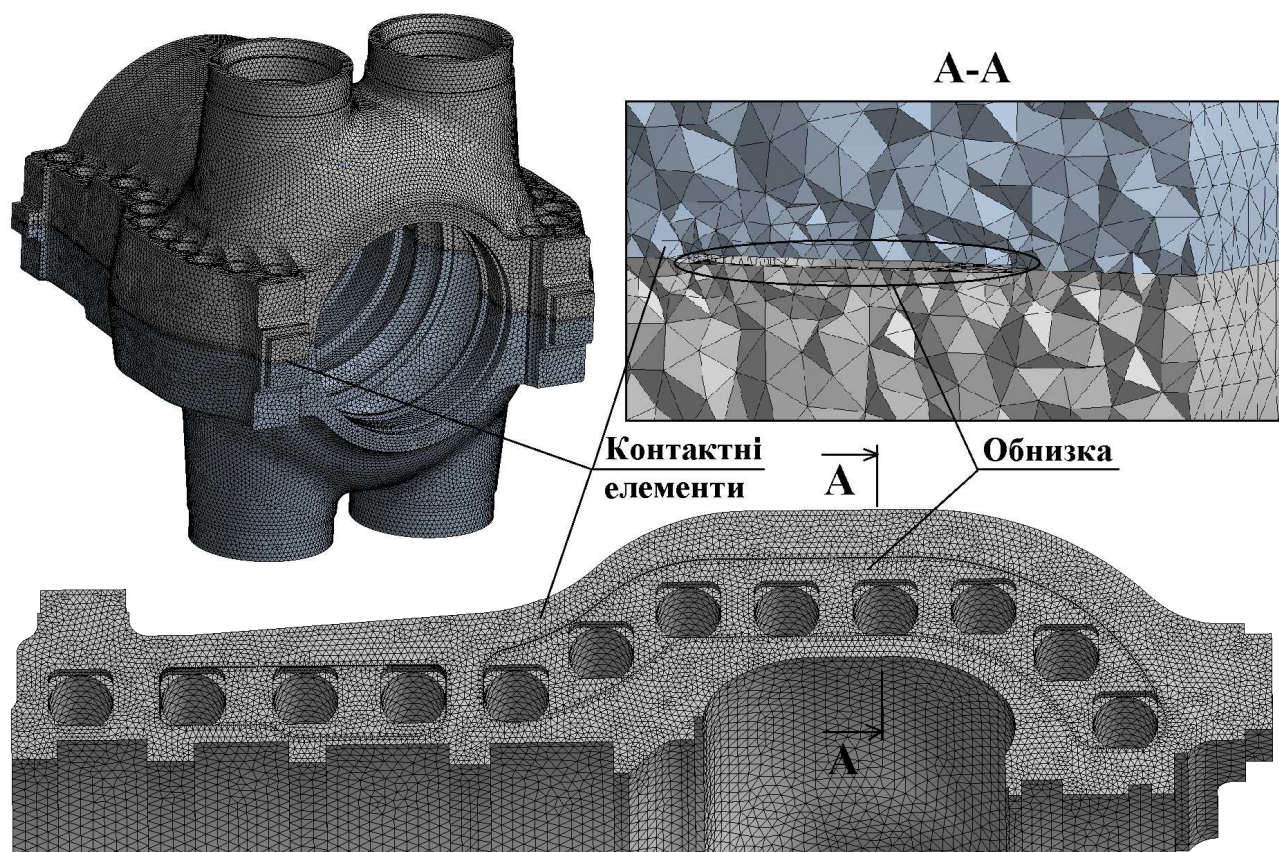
СЕ модель корпусу, адаптована для розв'язання контактної задачі: а – верхній і нижній корпусу в зборі; б – дзеркало фланцевого роз'єму; в – переріз фланця в області паровпуска.
